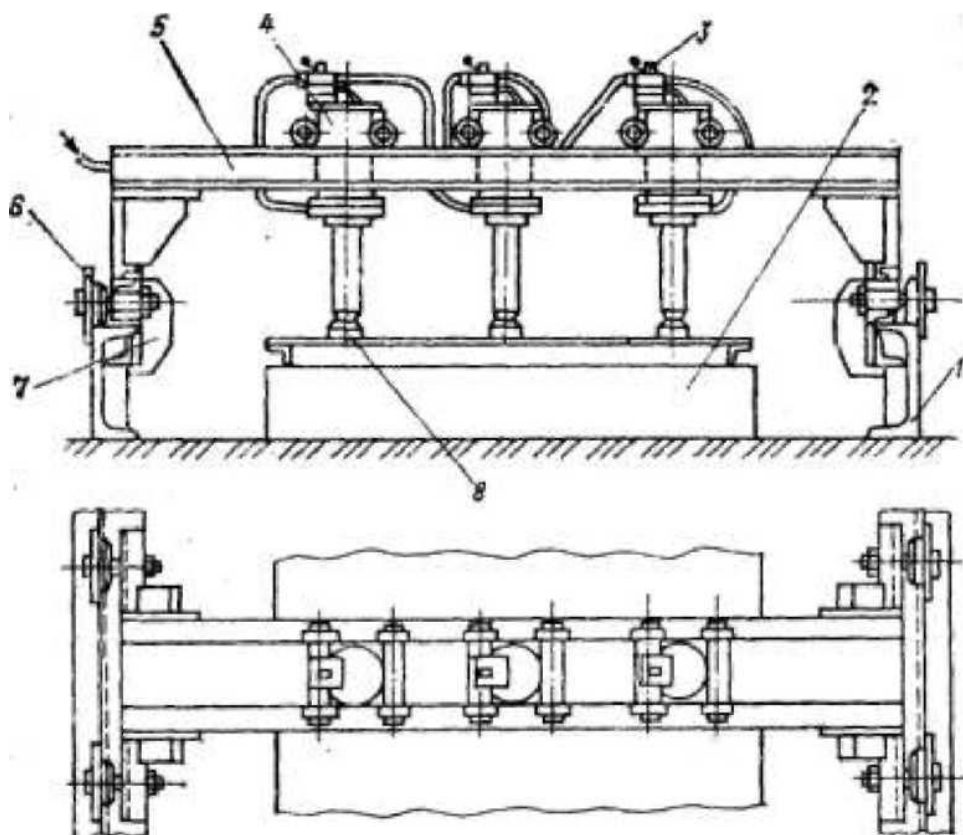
Стеллаж для сборки и сварки полотнищ
